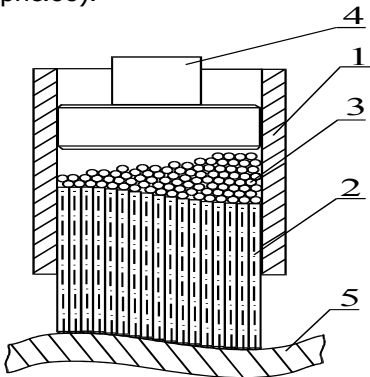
Схема многоконтактного виброударного инструмента ШСУ: 1 – корпус; 2 – стержни; 3 – стальные шары; 4 – боек; 5 – деталь
